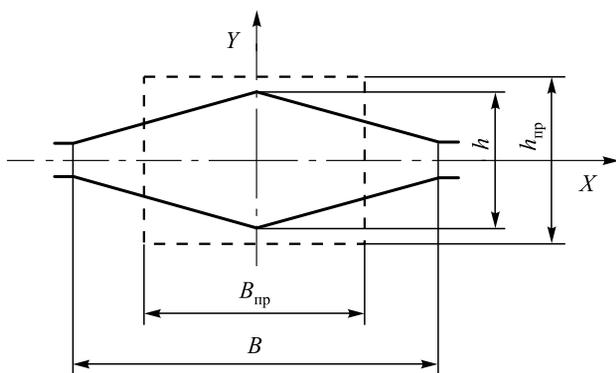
Схема вальцовки с калибровкой «прямоугольник – ромб»
